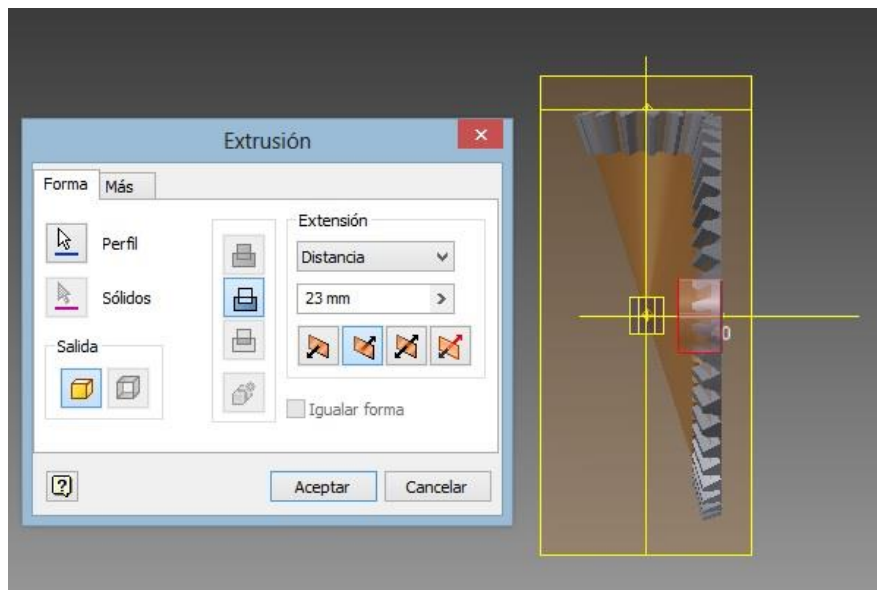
DETALLE EXTRUSIÓN PERFORACIÓN ENGRANAJE 2
